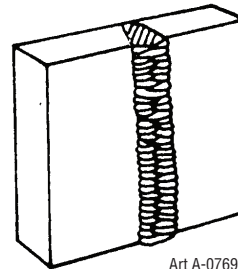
Position Verticale, soudure bout à bout
